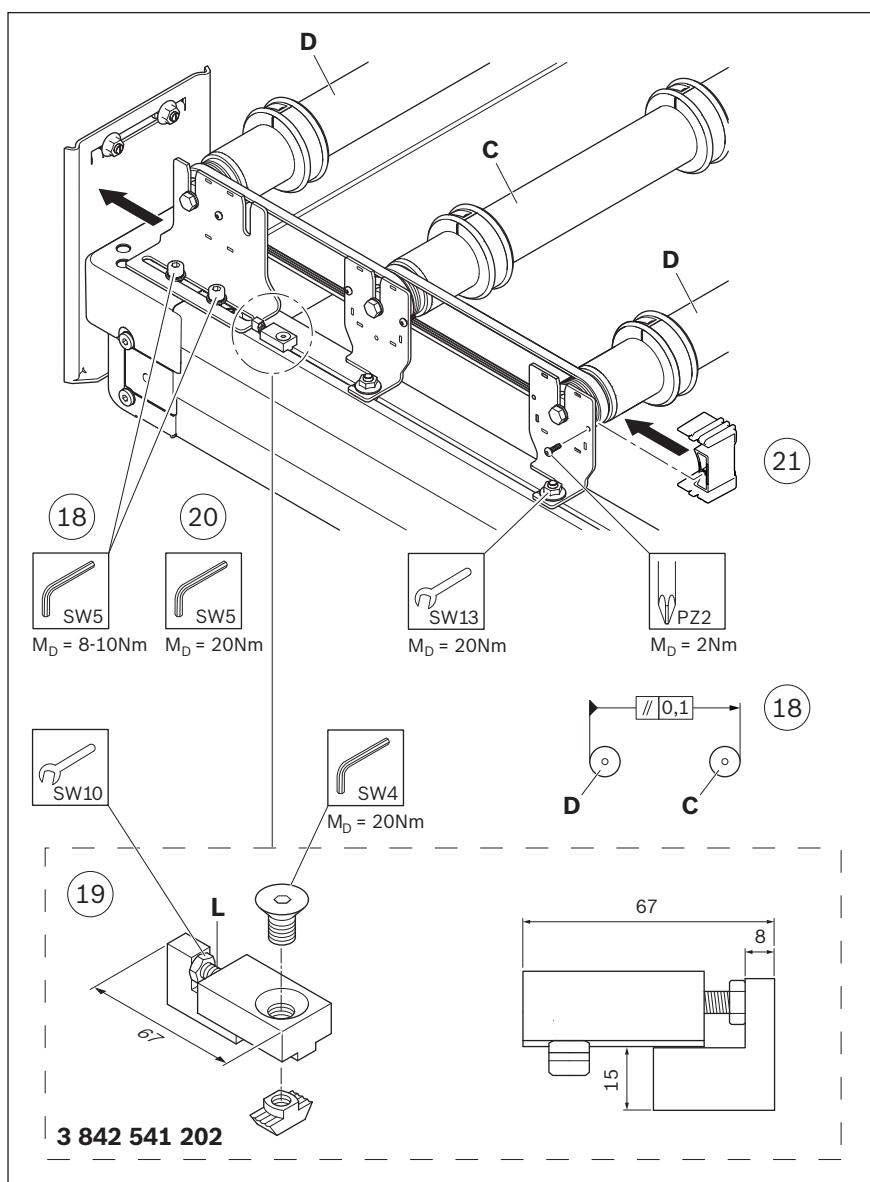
Cambio y montaje de la correa dentada y/o trapezoidal (3/4)
